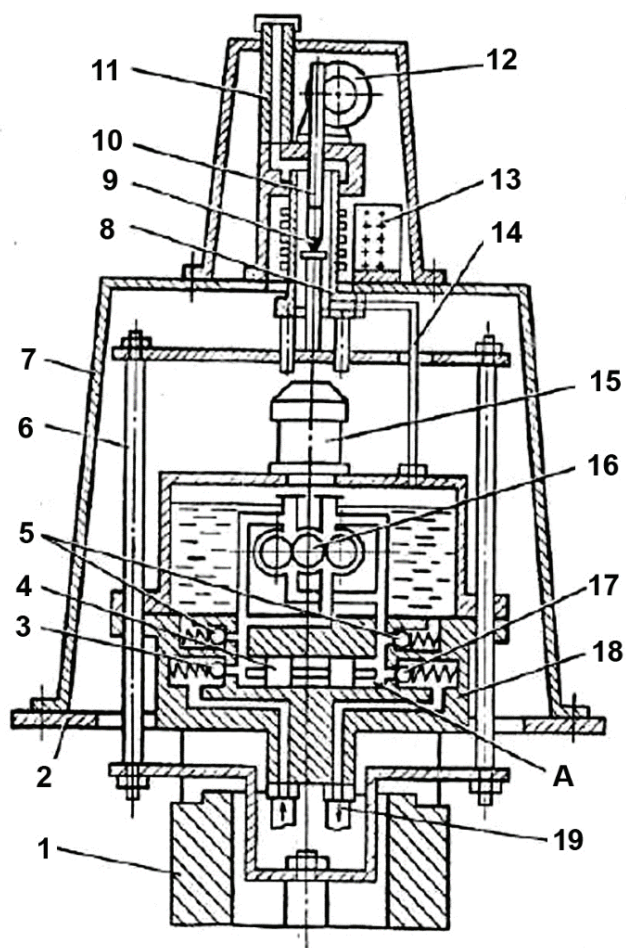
Схема гидравлического привода механизма разворота лопастей:
